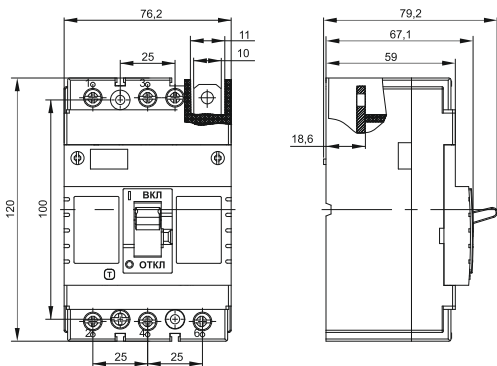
Габаритные и установочные размеры выключателя VA44-33 / Figure 6 — Overall and installation dimensions of the switch VA44-33 / 6-сурет — VA44-33 ажыратқышының габариттік және орнатқыш өлшемдері / Figura 6 — Dimensiunile generale și de montare ale întreruptorului VA44-33
